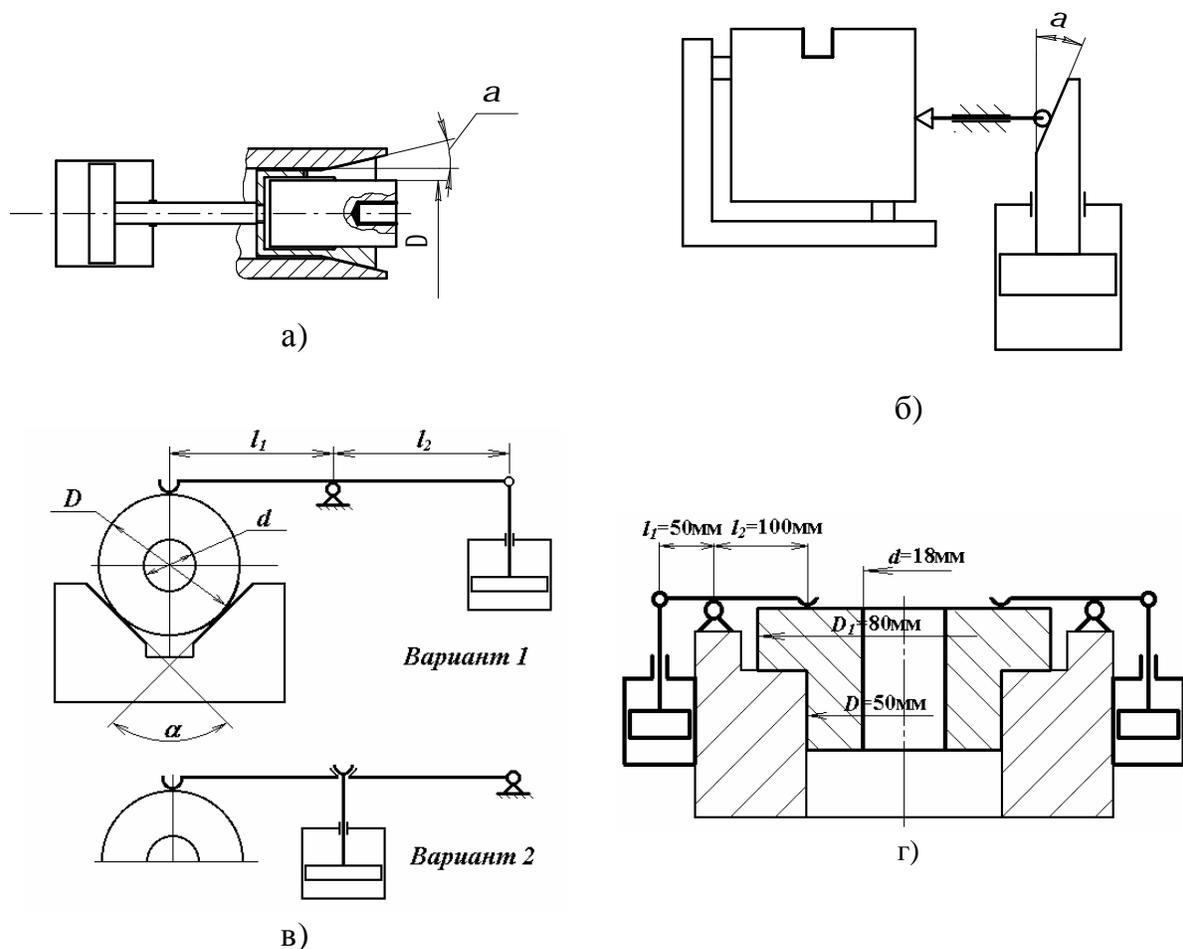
Принципиальные схемы приспособлений (а – с цанговым зажимным механизмом; б) с клиноплунжерным зажимным механизмом; в,г- с рычажными зажимными механизмами)
